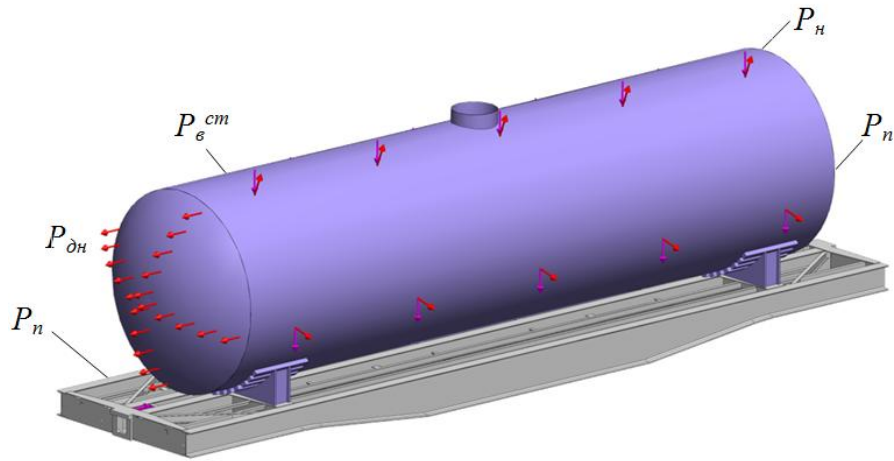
Розрахункова схема несучої конструкції вагона-платформи
